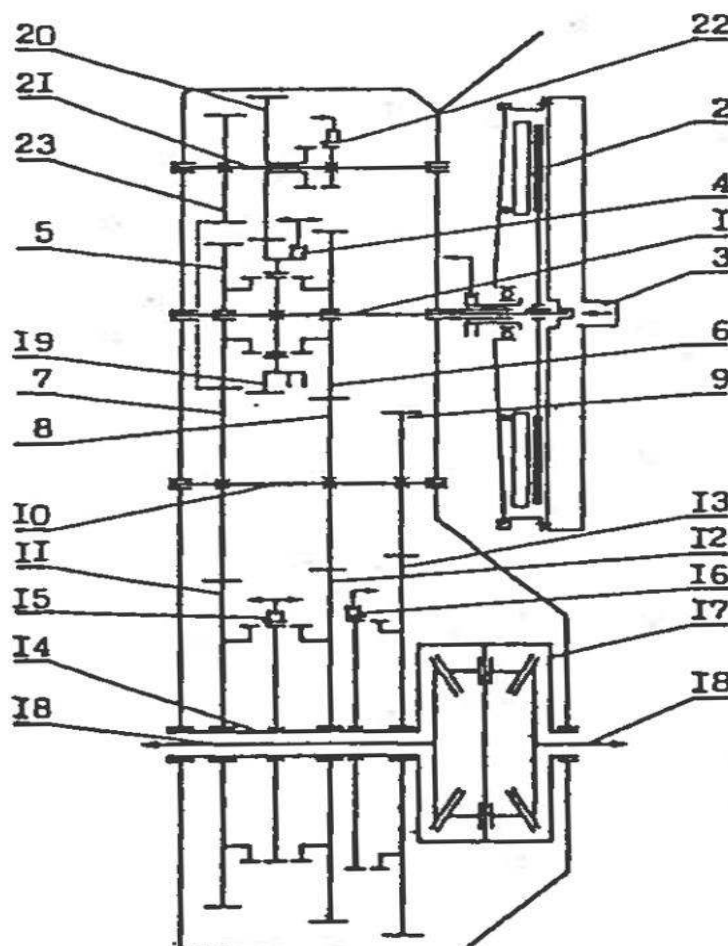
Кинематическая схема экспериментальной коробки передач
